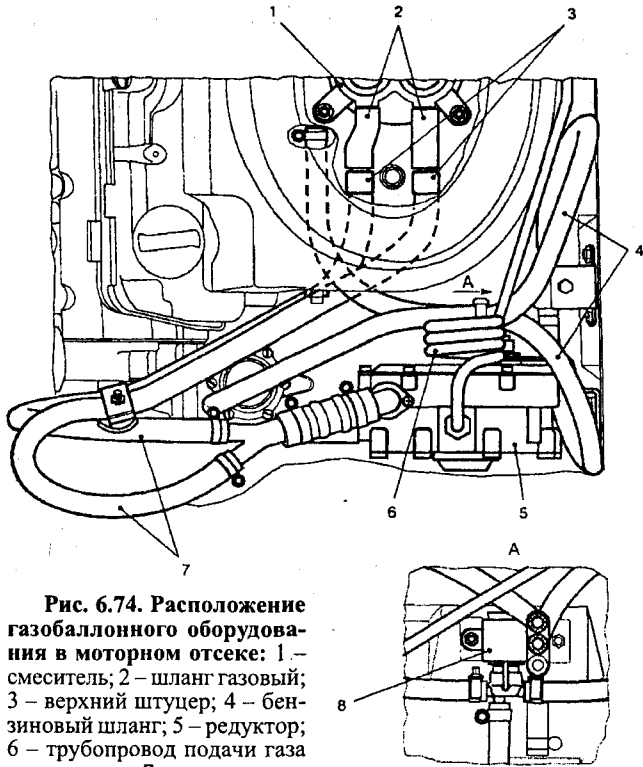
Расположение газобаллонного оборудования в моторном отсеке: 1 – смеситель; 2 – шланг газовый; 3 – верхний штуцер; 4 – бензиновый шланг; 5 – редуктор; 6 – трубопровод подачи газа к редуктору; 7 – шланг подачи газа к смесителю; 8 – клапан «бензин – газ»
